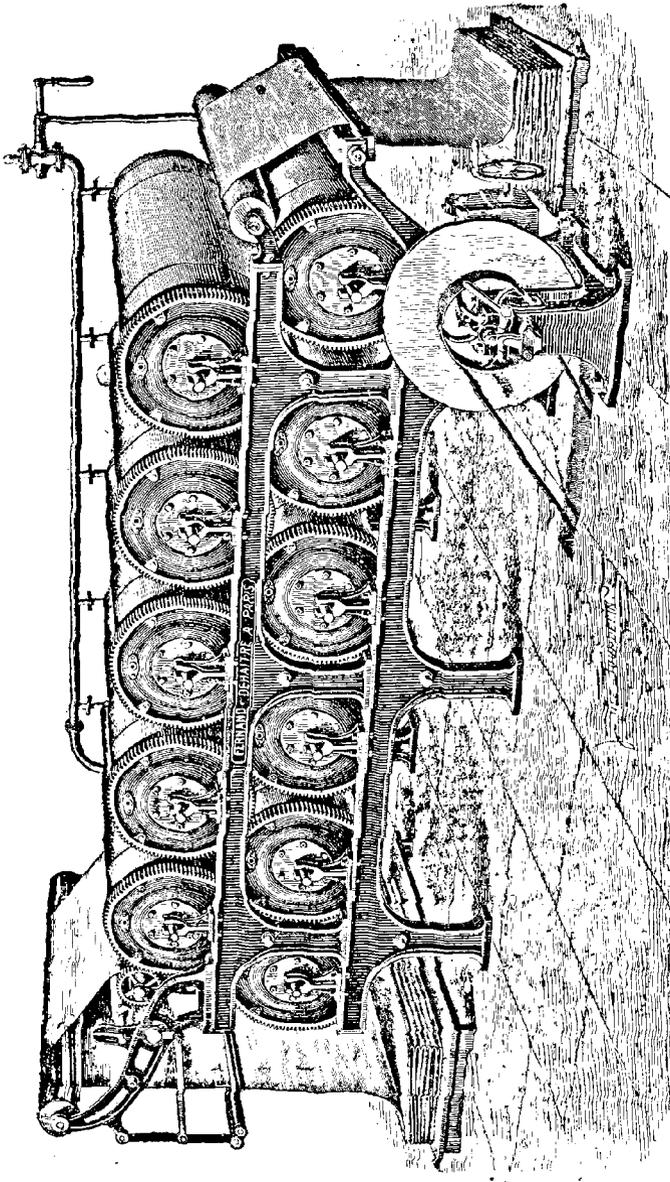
Tambour à 11 cylindres pour une largeur de pièce ; côté du moteur à friction.
